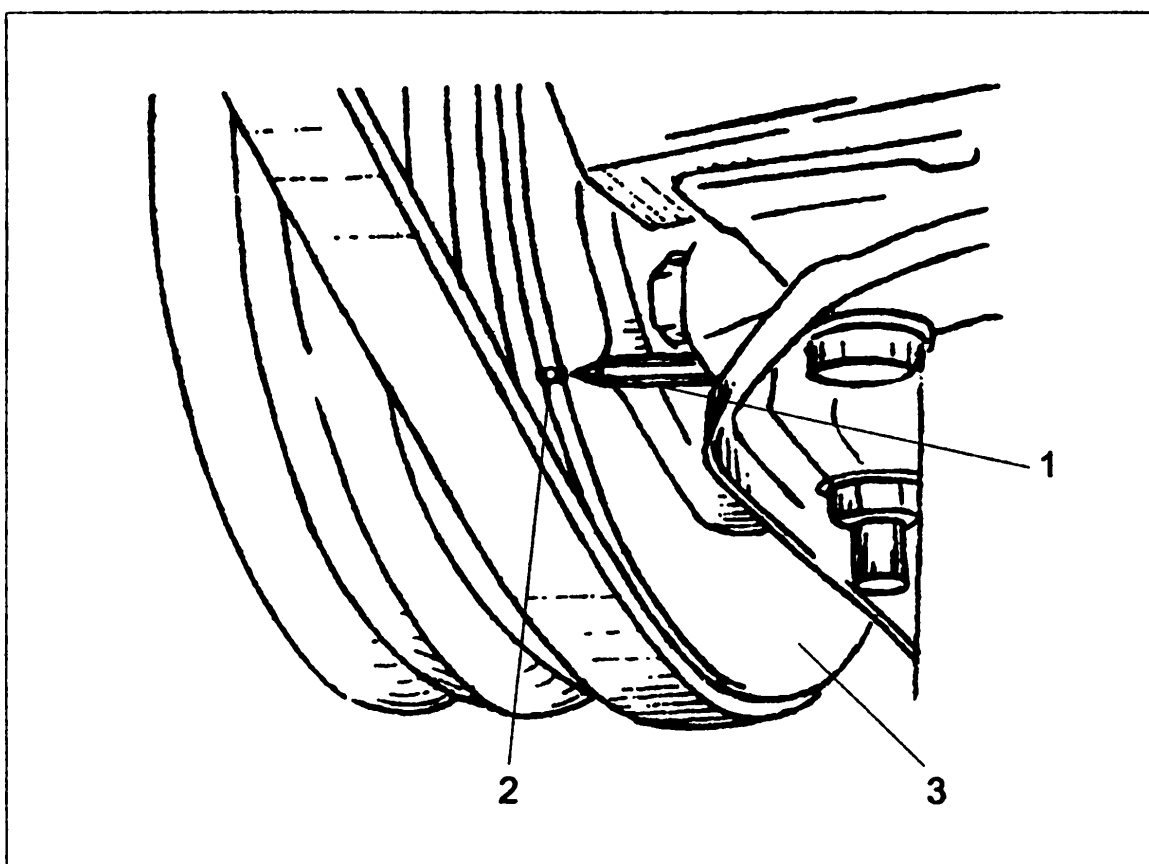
Метка на шкиве коленвала совпадает с указателем на корпусе двигателя:
